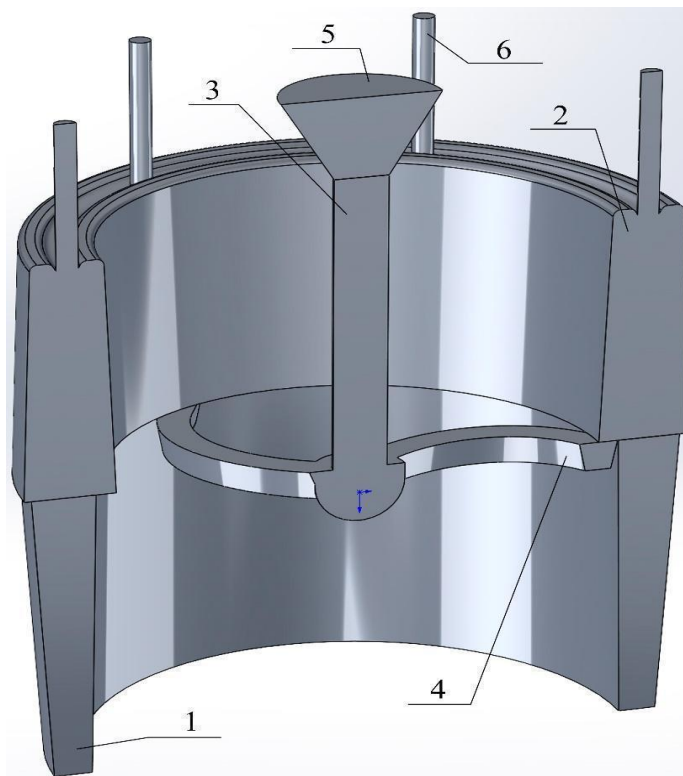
Модель оснастки виливка деталі «втулка»: 1 – модель виливка; 2 – модель прибілі; 3 – стояк; 4 – живильники; 5 – воронка для заливання металу; 6 – випора
